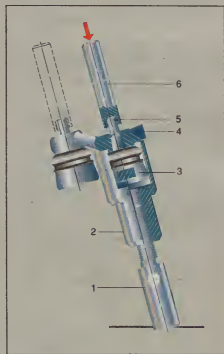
Разработанное автором приспособление для выпрессовки рулевого пальца из сошки (металлического рычага): 1 – винт; 2 – упор; 3 – корпус шарнира; 4 – сошка (металлический рычаг); 5 – палец; 6 – стержень.
